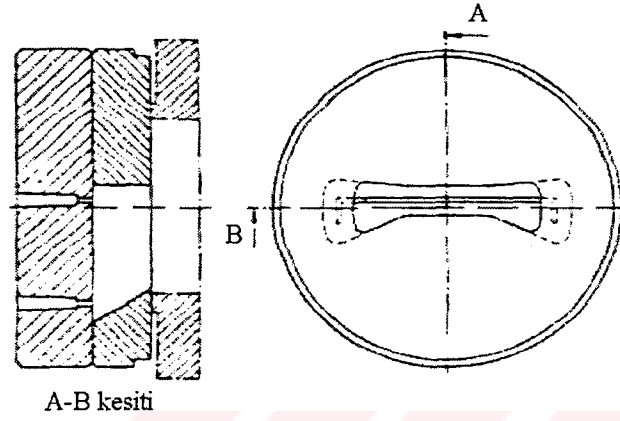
Üç parçalı besleyici plakalı kalıp; sol, besleme plakası; orta, kalıp; sağ, destek. /1/
